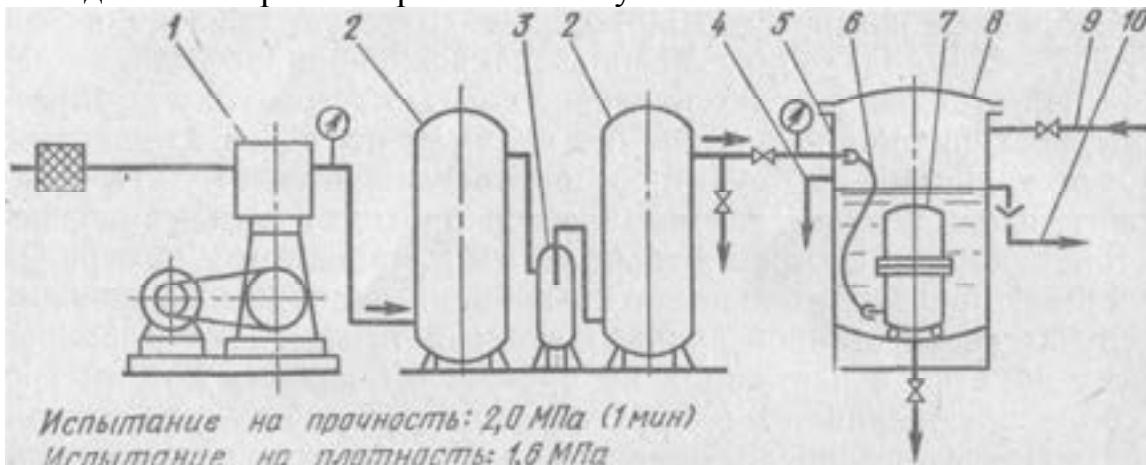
Испытание герметичного компрессора в броневанне после сварки кожуха:
